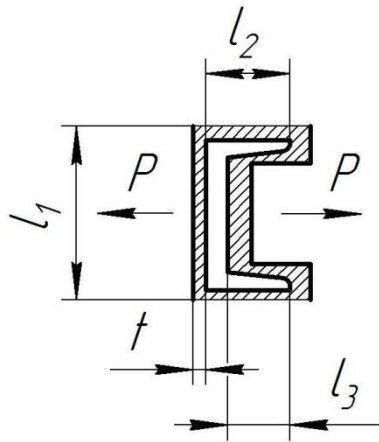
Розрахункова схема зварювального кріплення кронштейна до рами (вид загальний)
